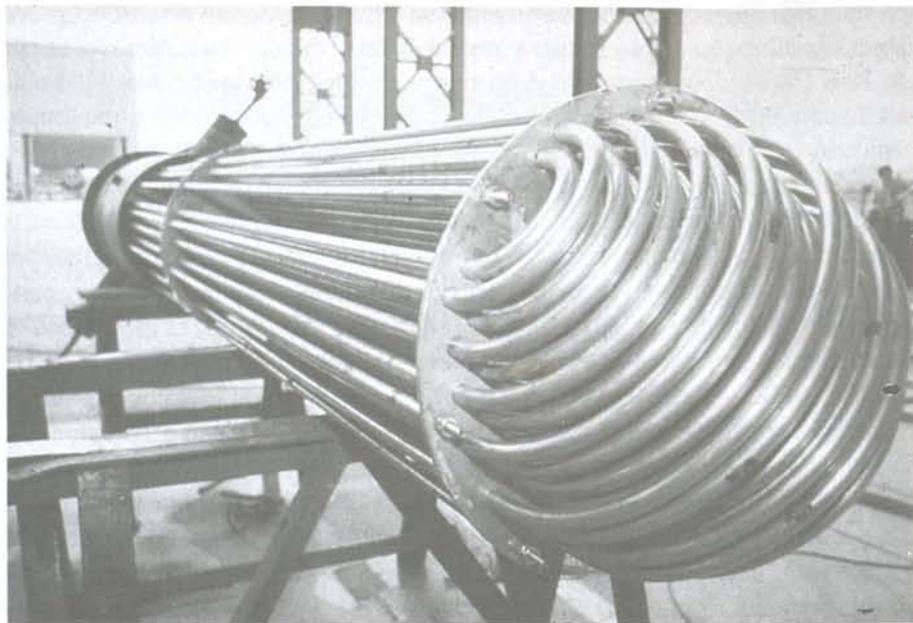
Feixe tubular em U desmontado. Cortesia da CONFAB Industrial S.A.
